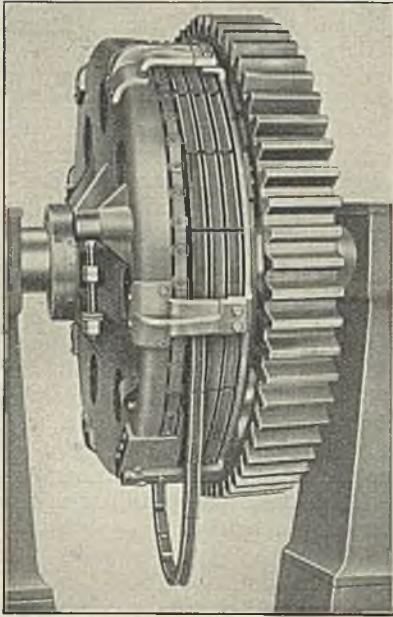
Schraubenrillenscheibe für einseitige Drehrichtung.
